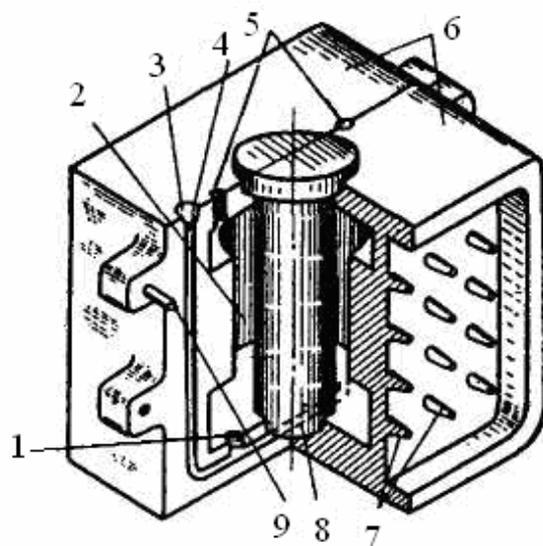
Конструкция кокиля: 1, 2 – половина кокиля; 3 – стержень; 4 – питатель; 5 – литниковая чаша; 6 – стояк; 7 – выпор
